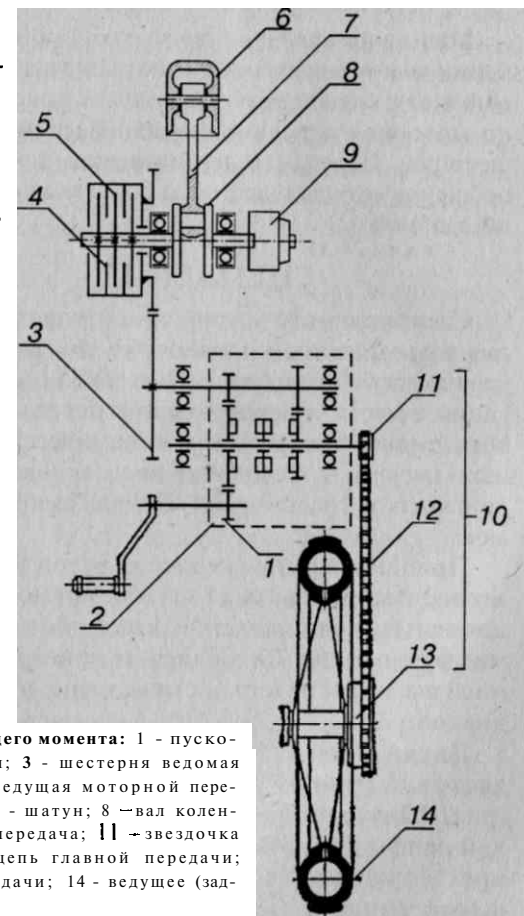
Схема передачи крутящего момента: 1 - пусковой механизм; 2 - коробка передач; 3 - шестерня ведомая моторной передачи; 4 - шестерня ведущая моторной передачи; 5 - сцепление; 6 - поршень; 7 - шатун; 8 - вал коленчатый; 9 - генератор; 10 - главная передача; 11 - звездочка ведущая главной передачи; 12 - цепь главной передачи; 13 - звездочка задняя главной передачи; 14 - ведущее (заднее) колесо
